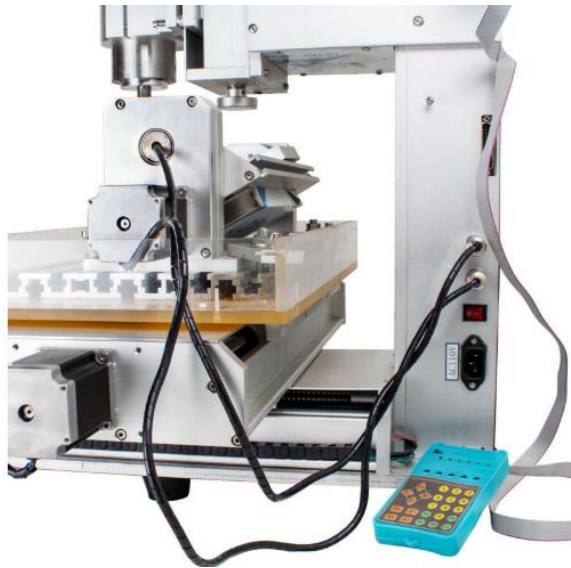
Parte interna de la fresadora Router CNC 5 Ejes
